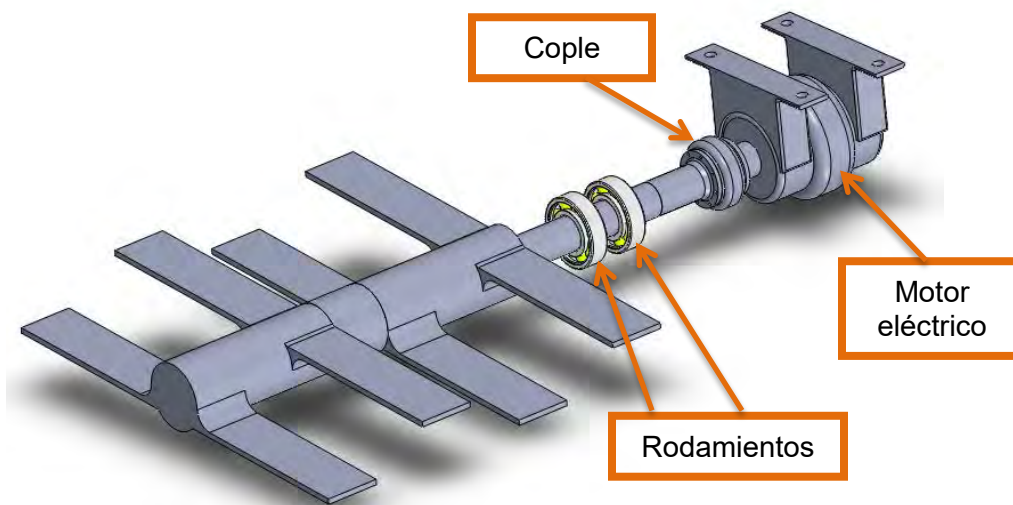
Motor eléctrico, Flecha motriz, cople y rodamientos del tipo bola
